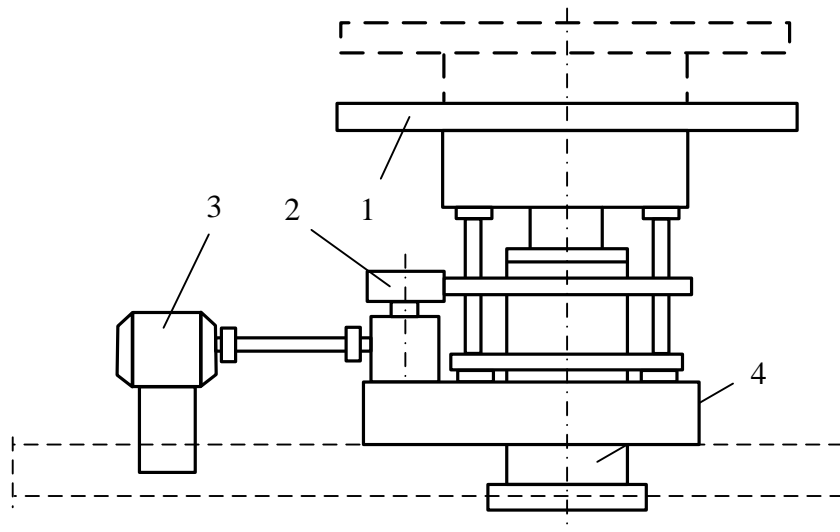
Схема поворотного стола промежуточного ковша: 1 – платформа промежуточного ковша; 2 – привод поворота; 3 – электродвигатель; 4 – гидроцилиндр подъема
